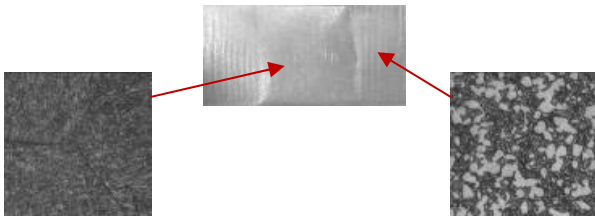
Внешний вид и микроструктура сварного шва по сравнению с основным металлом
